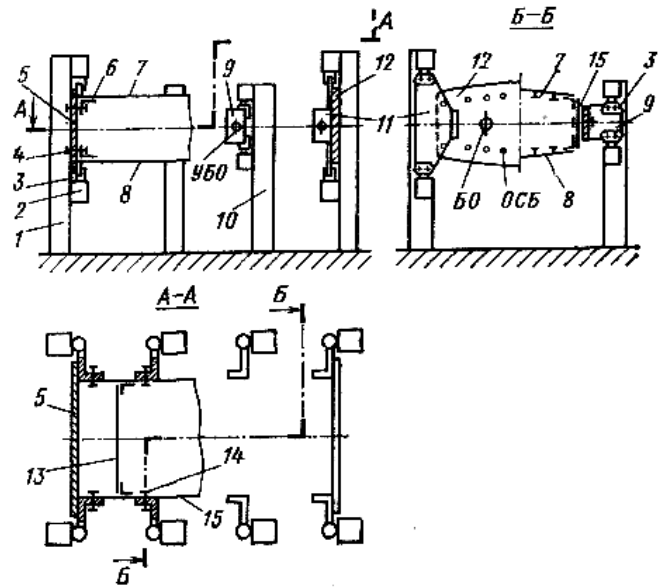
Упрощенное сборно-разборное приспособление для сборки кессона центроплана
